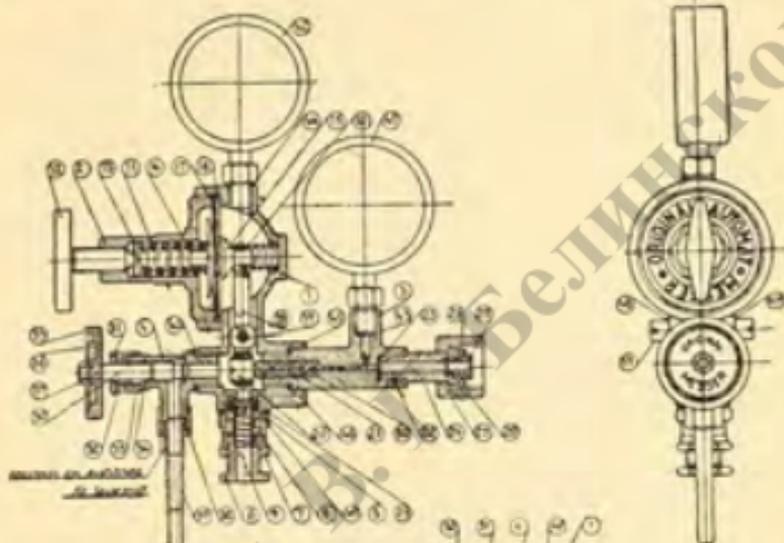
Механизм баллона. На чертеже известно: 1—приспособление для прикрепления всего механизма к баллону. 2—регулирующий винт редуктора. 3—часть редукционного приспособления. 4—манометр (финиметр). 5—манометр рабочего давления. 6—присоединение к рукаву. 7—предохранительный клапан.
